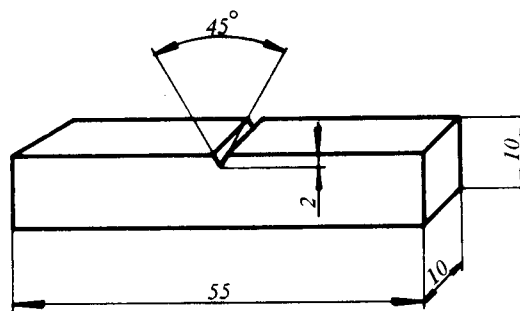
Dimensions de l'éprouvette pour essais de choc
